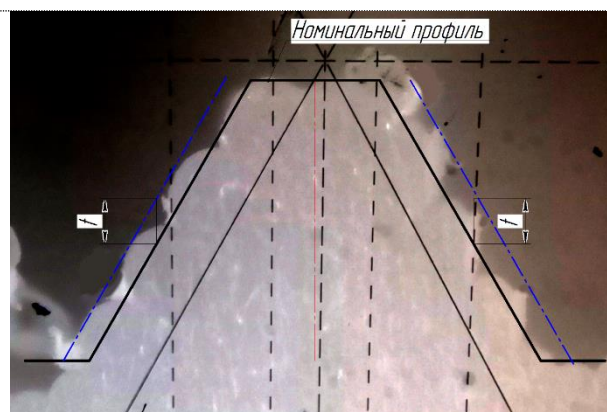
Профиль резьбы M14 сформированной в образце из PETG-пластика
